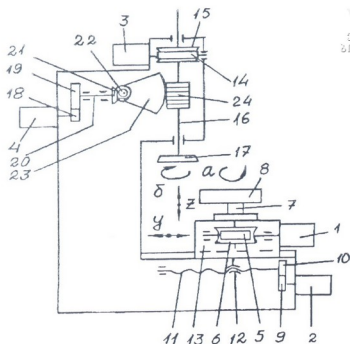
Кинематическая схема зубодолбежного станка с ЧПУ для нарезания некруглых, круглых цилиндрических колес
